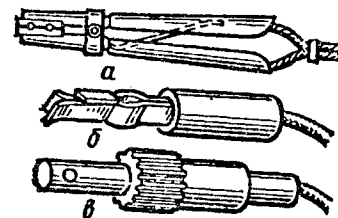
Электрододержатели для ручной дуговой сварки: *a* — пружинный; *б* — пластинчатый; *в* — винтовой
